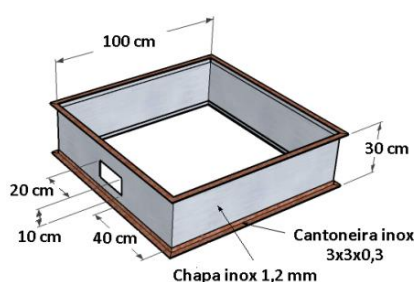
Módulo 4 ou base metálica para a construção da câmara de resfriamento (veja a abertura para entrada de parte do ar primário).
